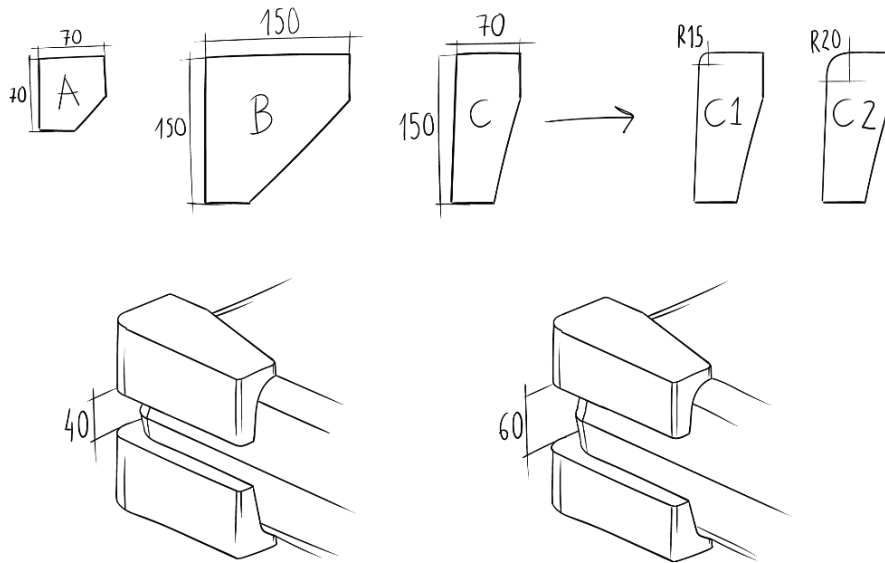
Bocetos de las propuestas para cantoneras
